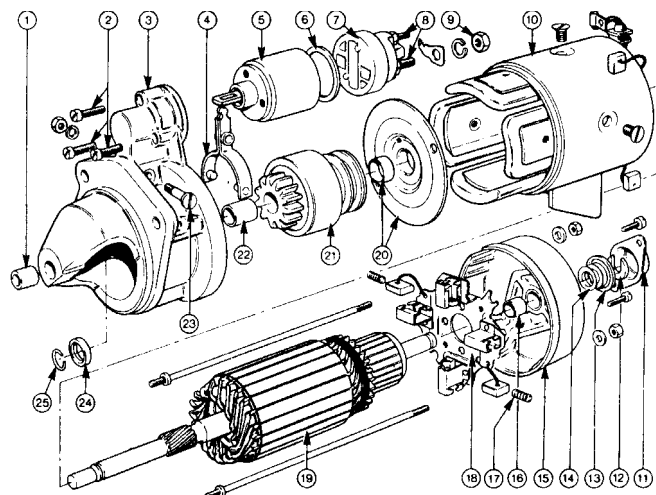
Стартер BOSCH JF 2 кВт. 1 - Втулка. 2 - Винт крепления. 3 - Корпус привода. 4 - Вилка привода. 5 - Корпус. 6 - Прокладка. 7 - Крышка. 8 - Клеммы. 9 - Гайка. 10 - Основной корпус. 11 - Колпачок. 12 - С-образный зажим. 13 - Прокладка. 14 - Шайбы. 15 - Крышка. 16 - Втулка. 17 - Пружина щетки. 18 - Коробка щетки. 19 - Якорь. 20 - Подшипник и пластина. 21 - Обгонная муфта. 22 - Втулка. 23 - Ось вилки. 24 - Втулка. 25 - С-образный зажим.
